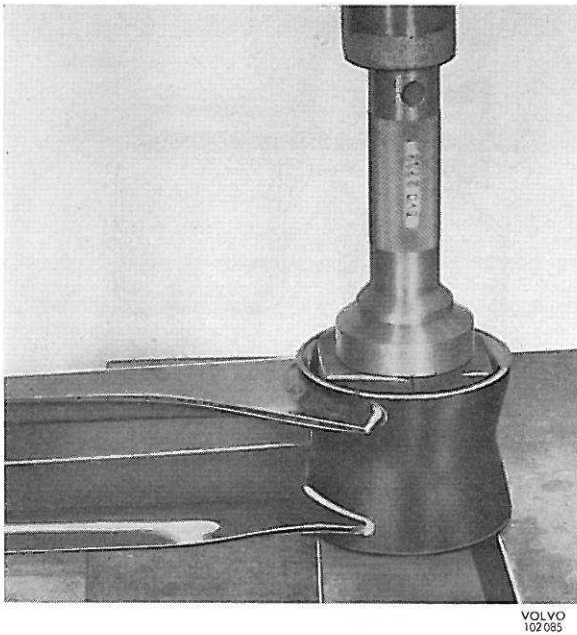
Démontage (et montage) de la bague avant, bras de roue
